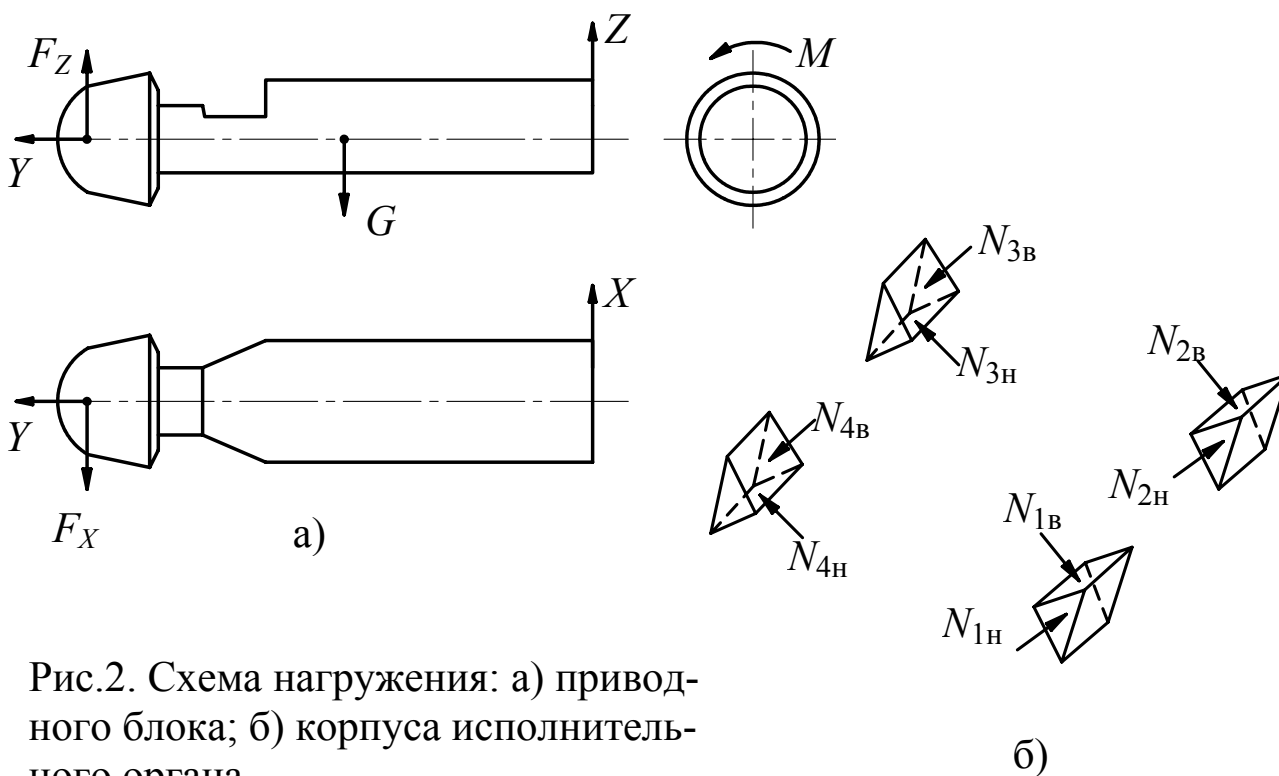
Схема нагружения: а) приводного блока; б) корпуса исполнительного органа
